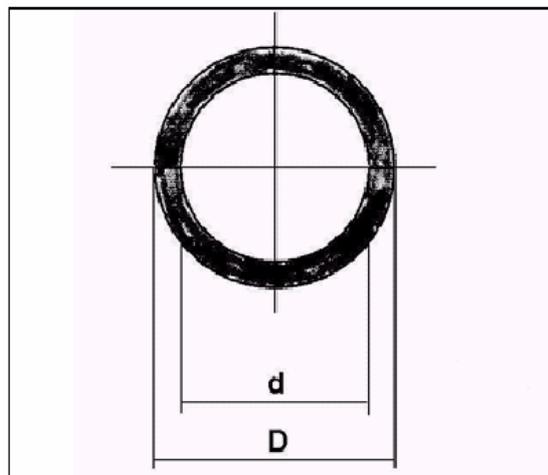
Innen- und Aussendurchmesser eines Mastrohres
